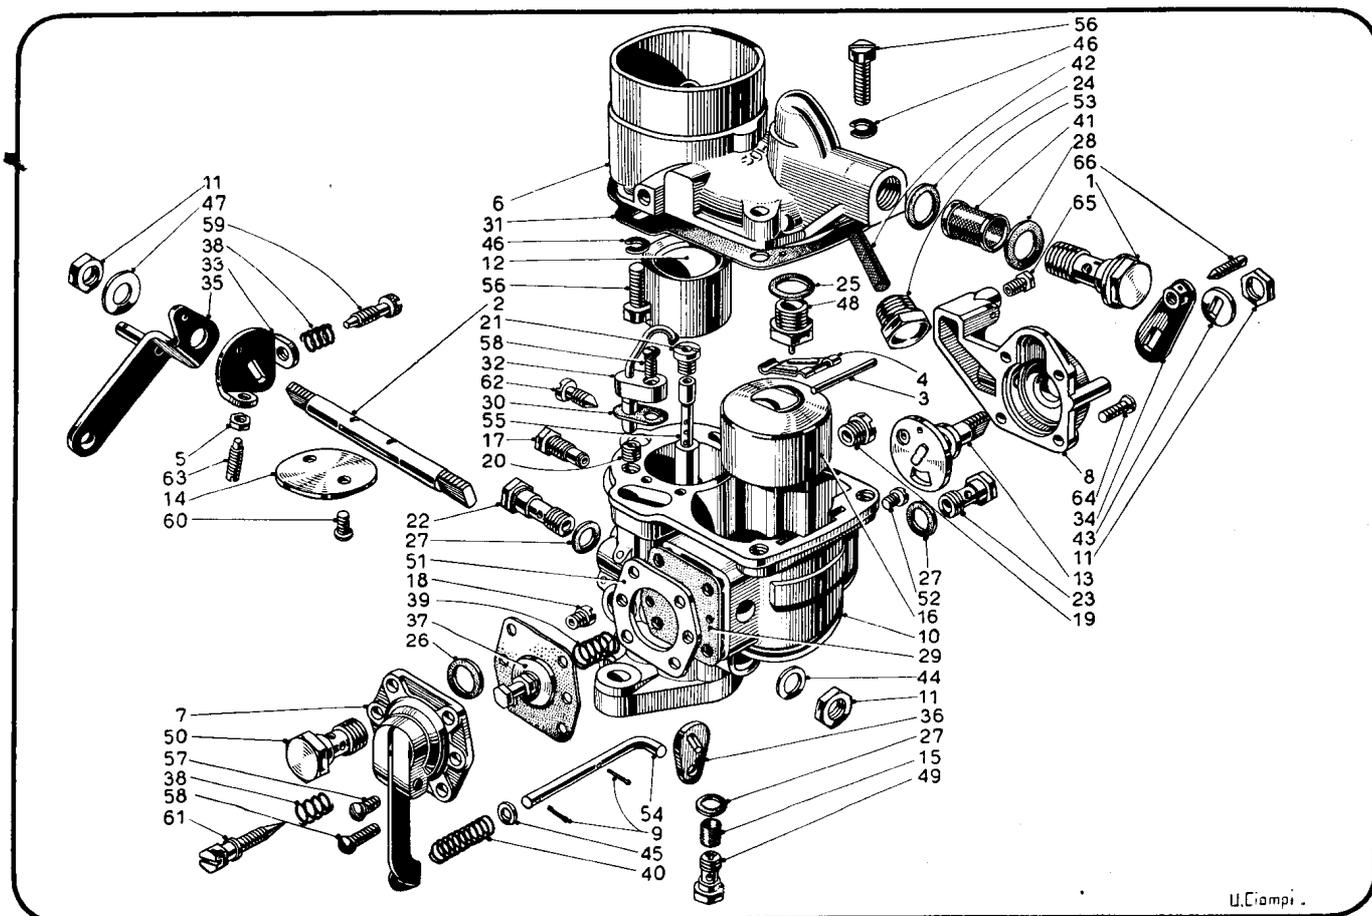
/30 - Carburatore per motori 2" e 3" serie (Dal Cata'ogo parti di ricambio).
